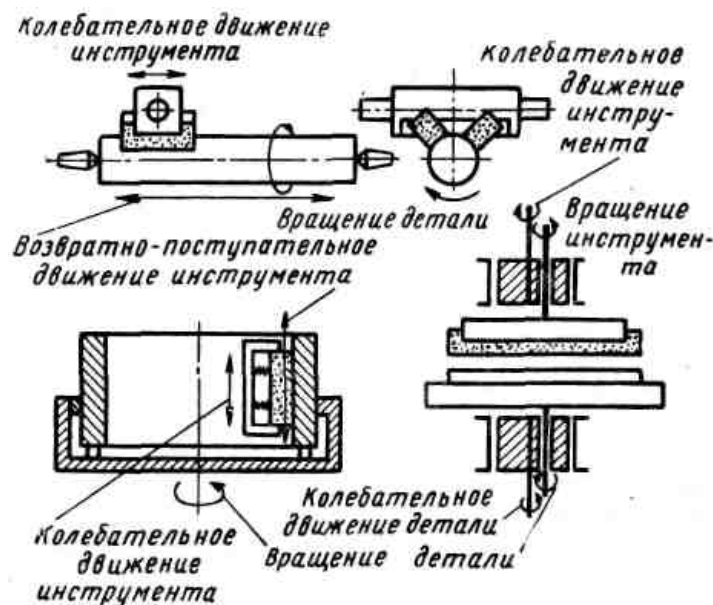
Схемы движения инструмента и заготовки при суперфинишировании
